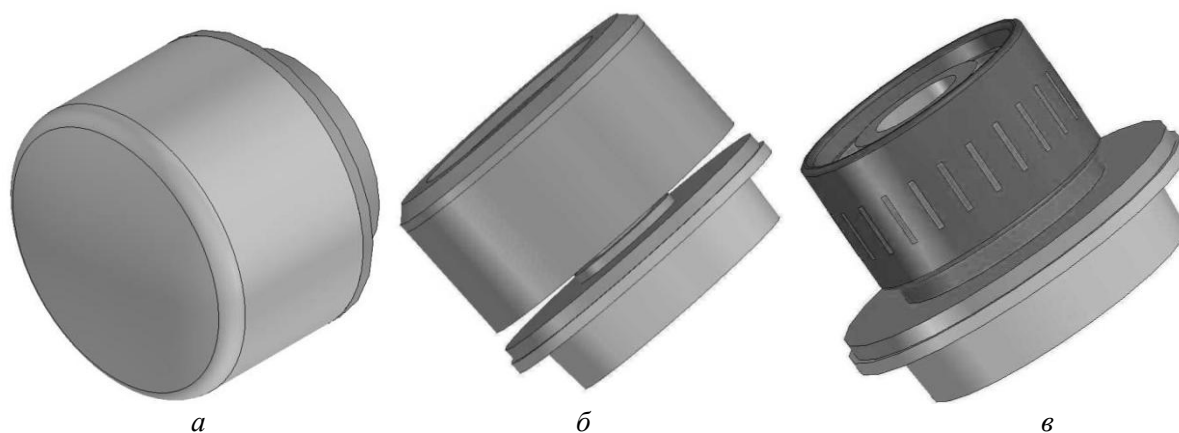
Под сборки двигателя-маховика при проведении анализа
